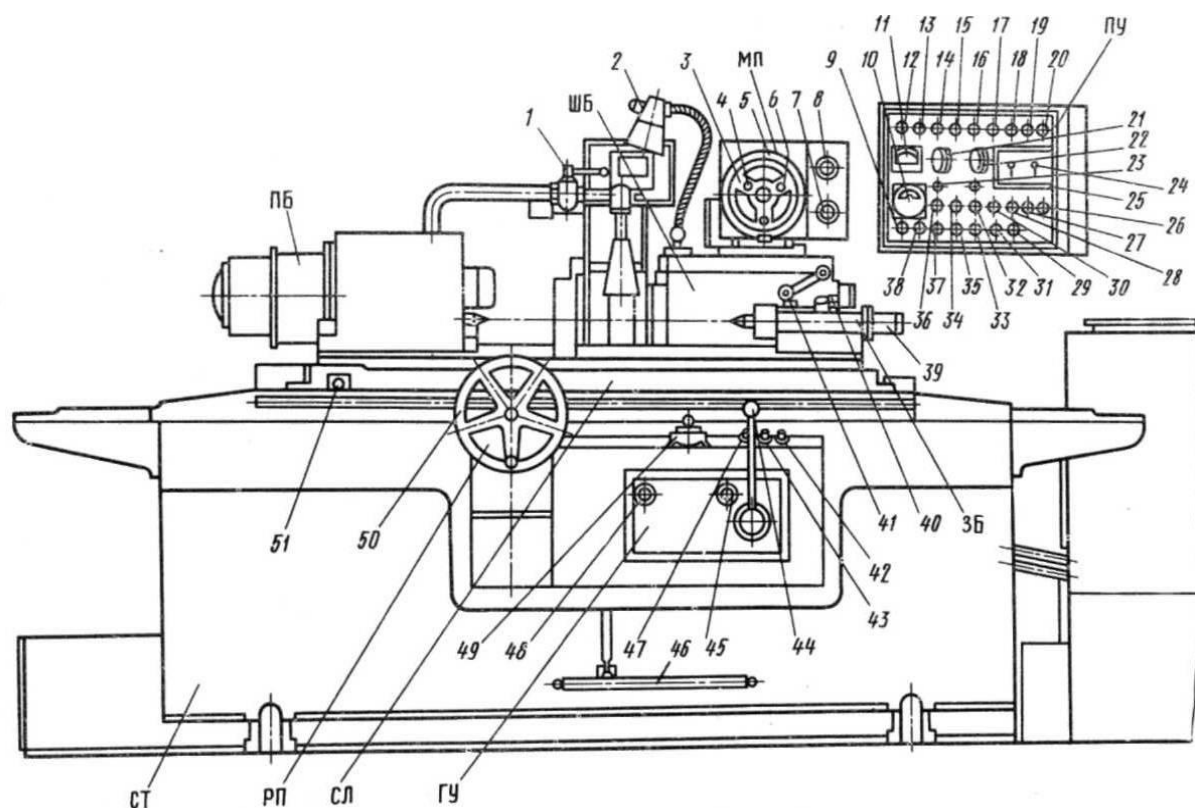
Основные части и органы управления круглошлифовального станка модели 3М151
